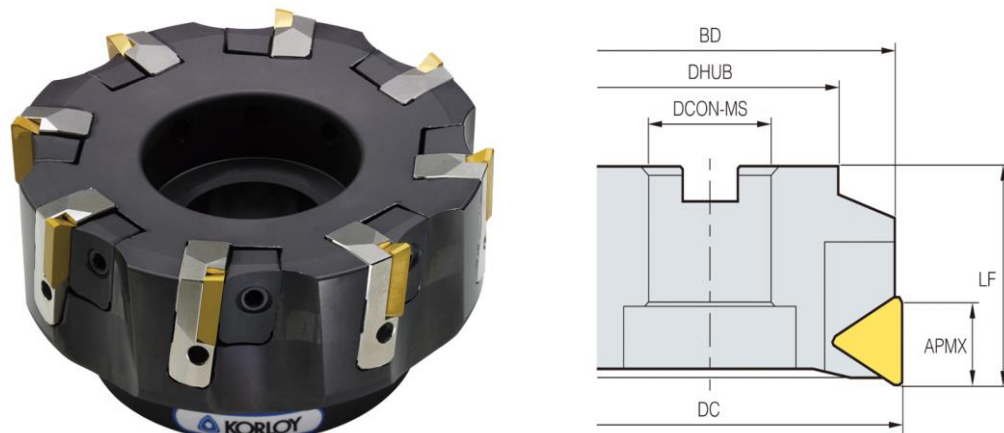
Фреза торцева Karloy MaxMill [15]
